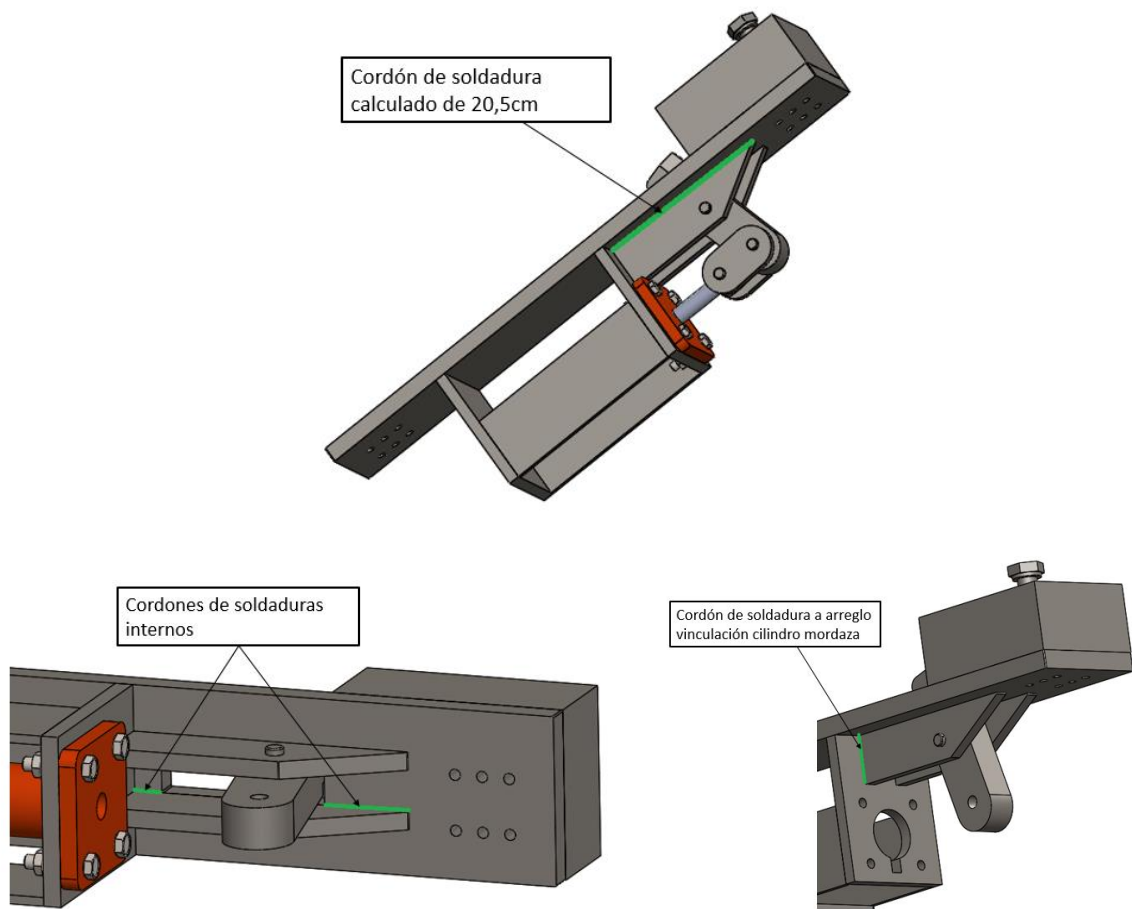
Cordones de soldadura de agarre mordaza a planchuela carro.
